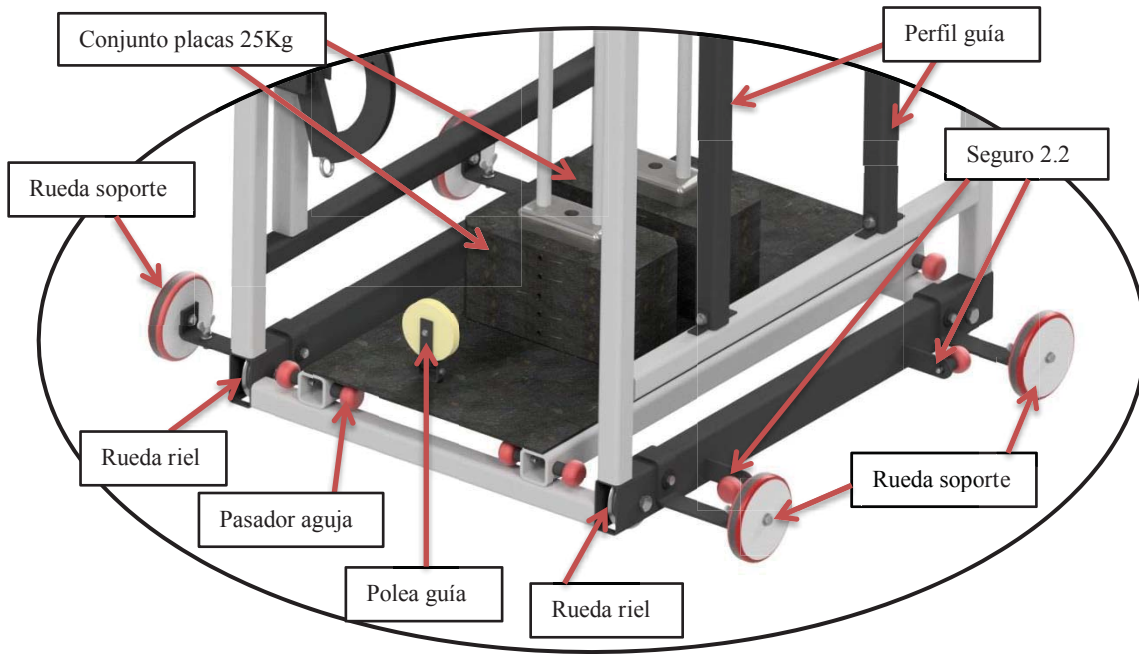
Detalle C, elementos que componen la zona inferior de la estructura A (2.1).
